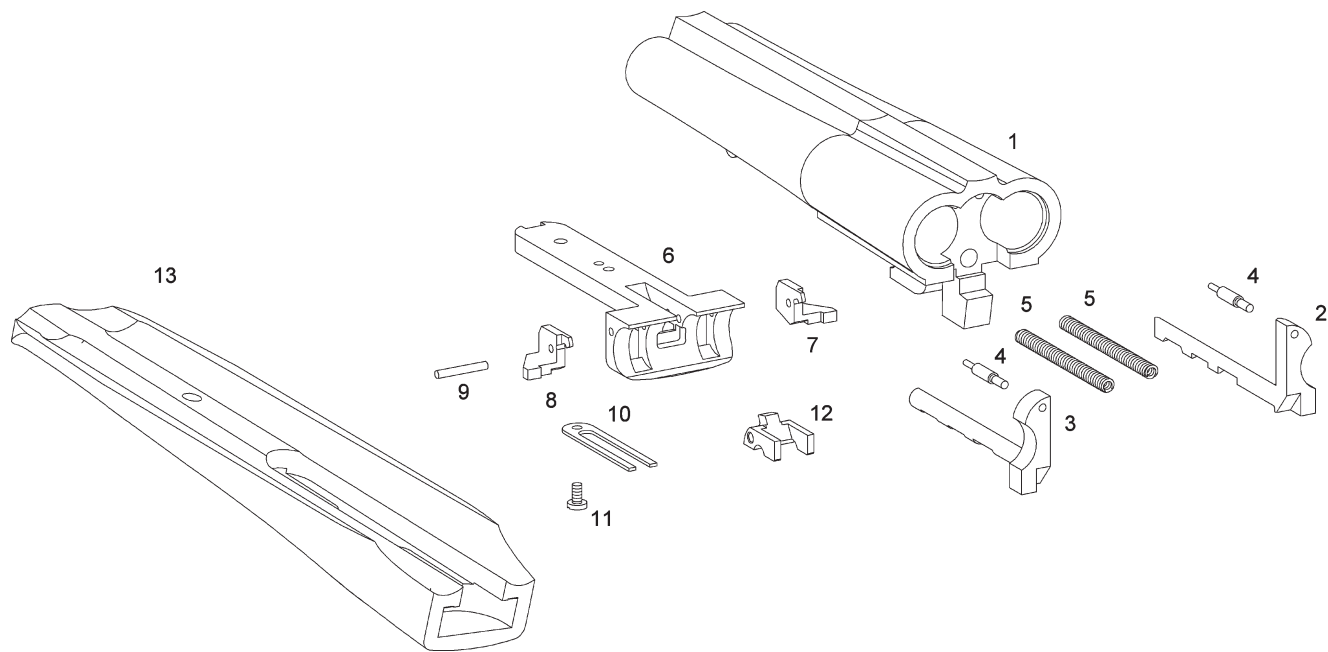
Детали выбрасывающего механизма ружей МР-43Е, МР-43Е-1С
